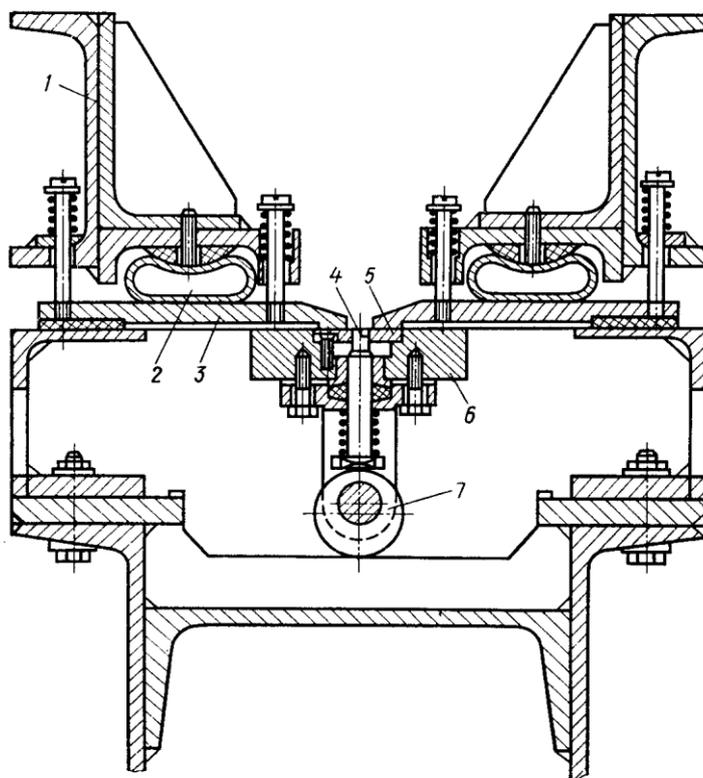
Приспособление для сборки и сварки прямолинейных стыков тонколистовых элементов
